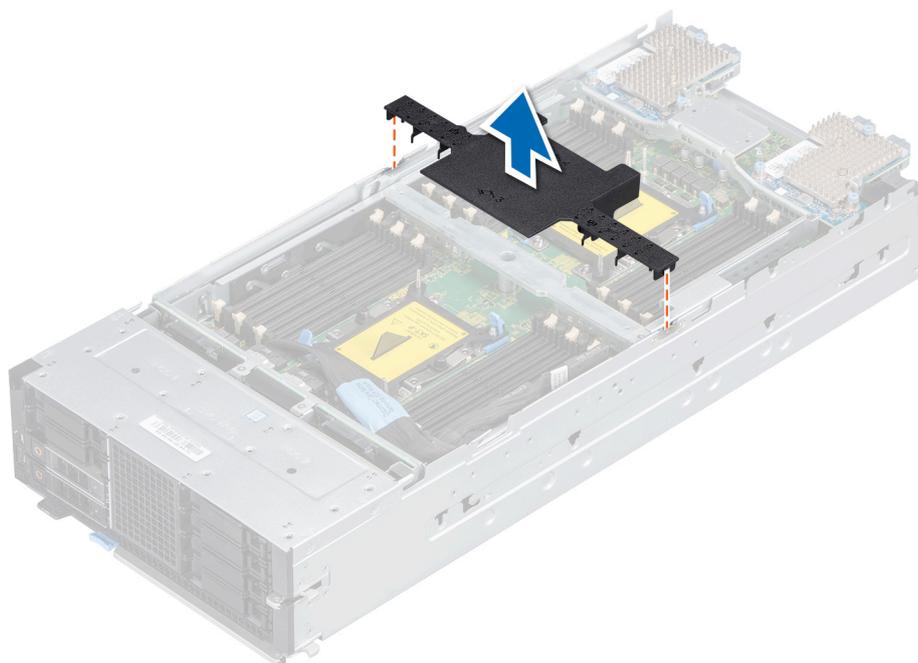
Entfernen des Kühlgehäuses vom PEM
